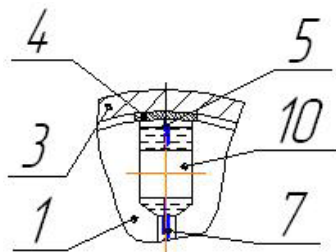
Вариант исполнения устройства для автобалансировки заготовок с балансировочными цилиндрами
